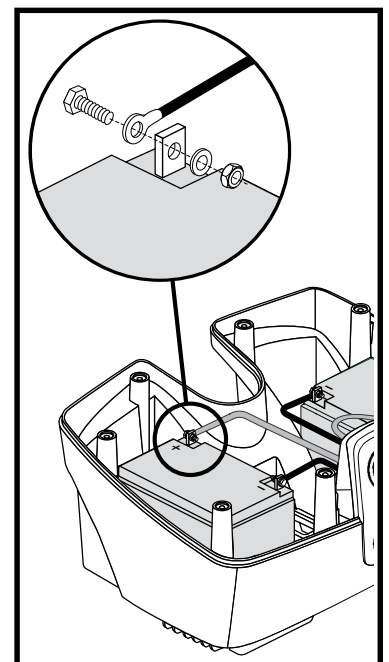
Scollegare il cavo batteria dalla scatola batteria 17-22 Ah
